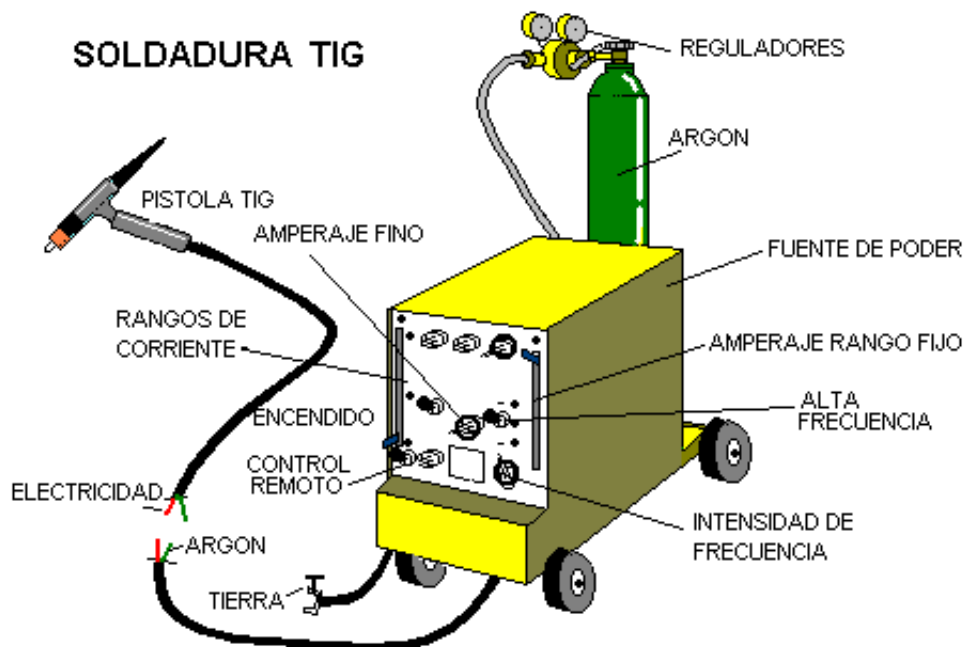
Equipo de soldadura GTAW. [38]
